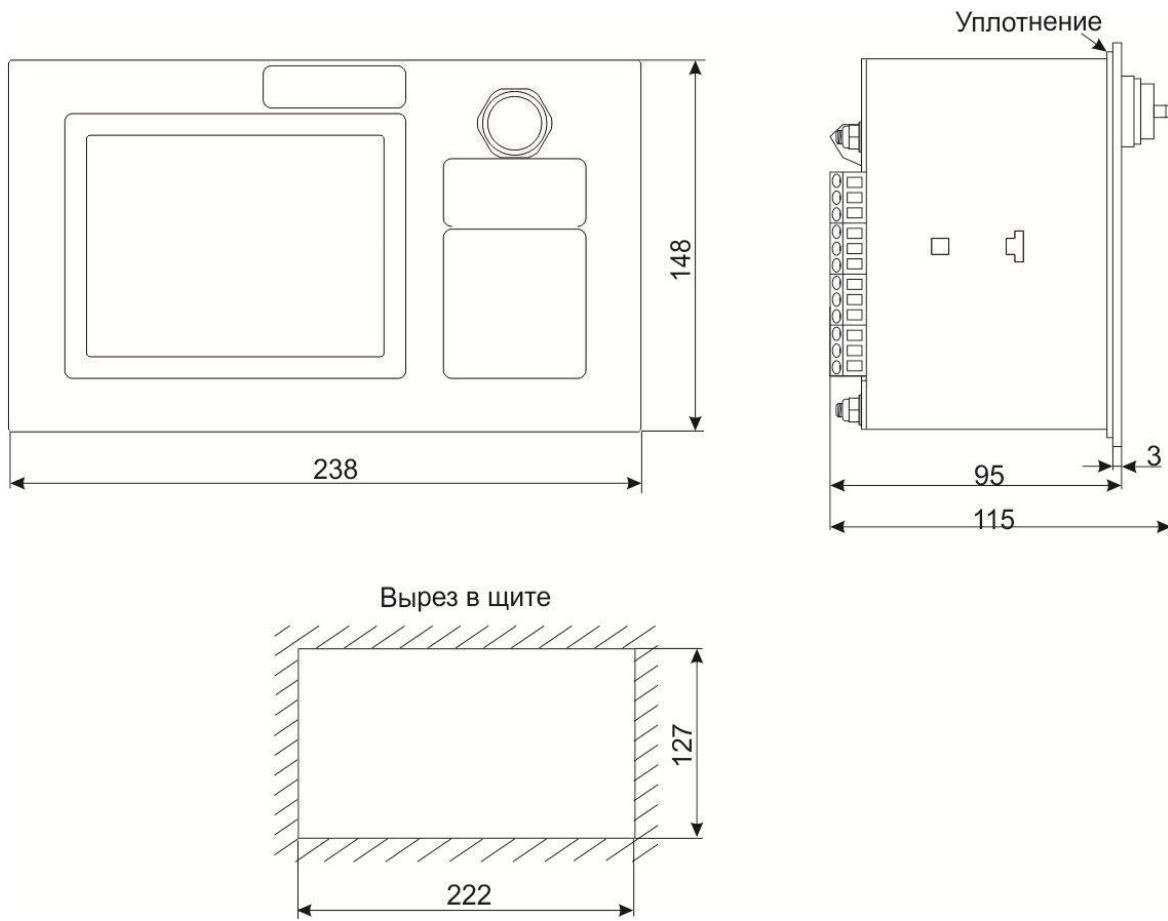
Габаритные размеры основного блока прибора Термодат-29Е6/..../F/IP67
